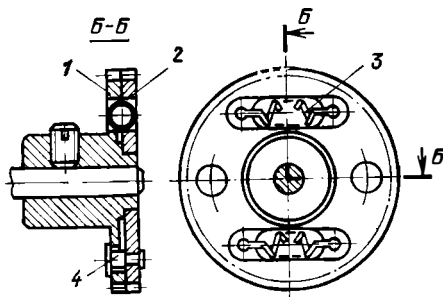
Конструкция разрезных зубчатых колес: 1 — неподвижное ЗК; 2 — подвижное ЗК; 3 — пружина; 4 — заклепка
